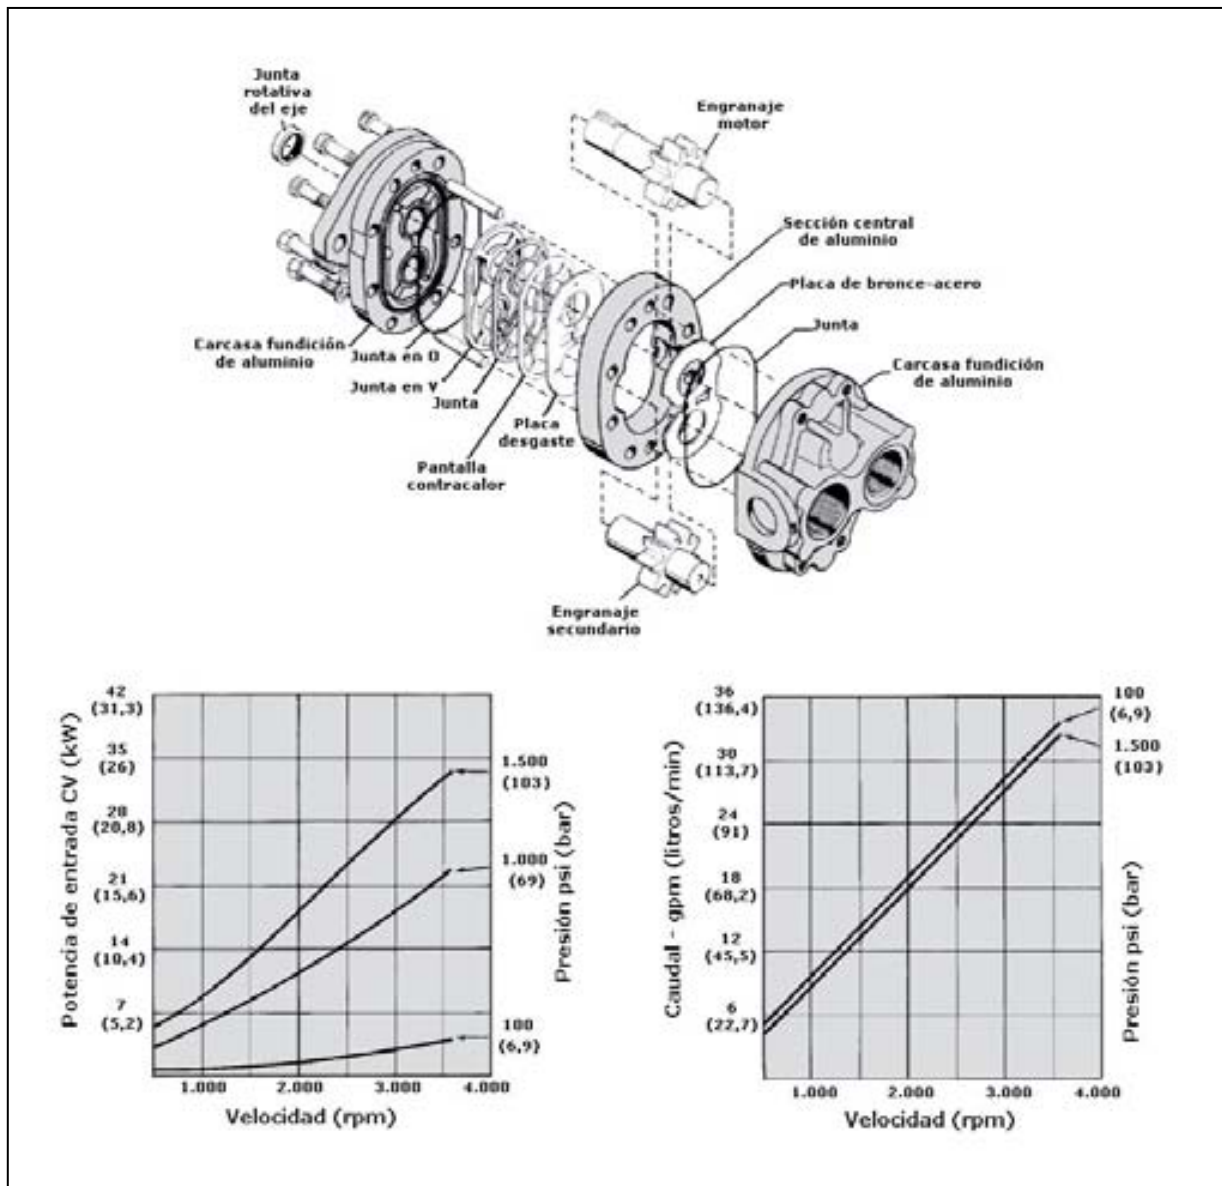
Despiece y curvas características del motor de engranajes. Fuente: Parker Hannifin
